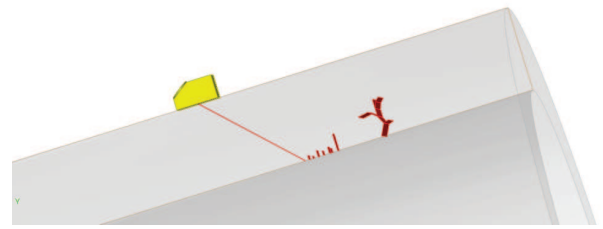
Rede de fissuras e fissura ramificada numa tubulação.
